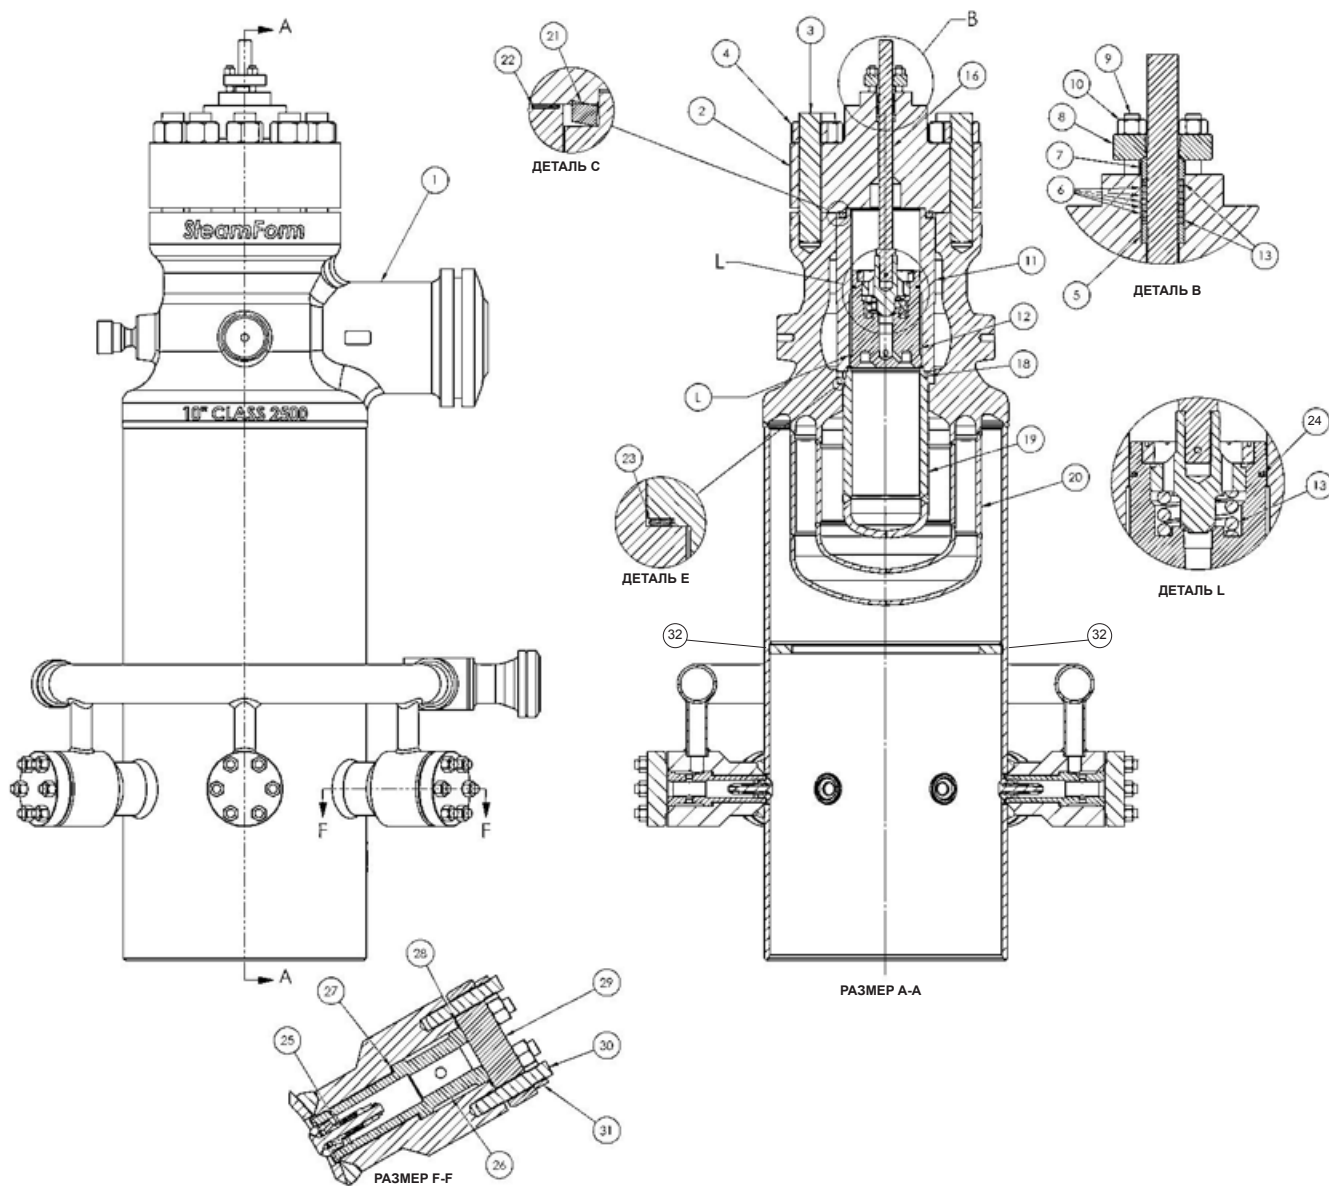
4-х ступенчатый угловой корпус клапана SteamForm с конструкцией пробки с управляющим клапаном, вставным диффузором второй ступени и сварными диффузорами для ступеней 3 и 4.
